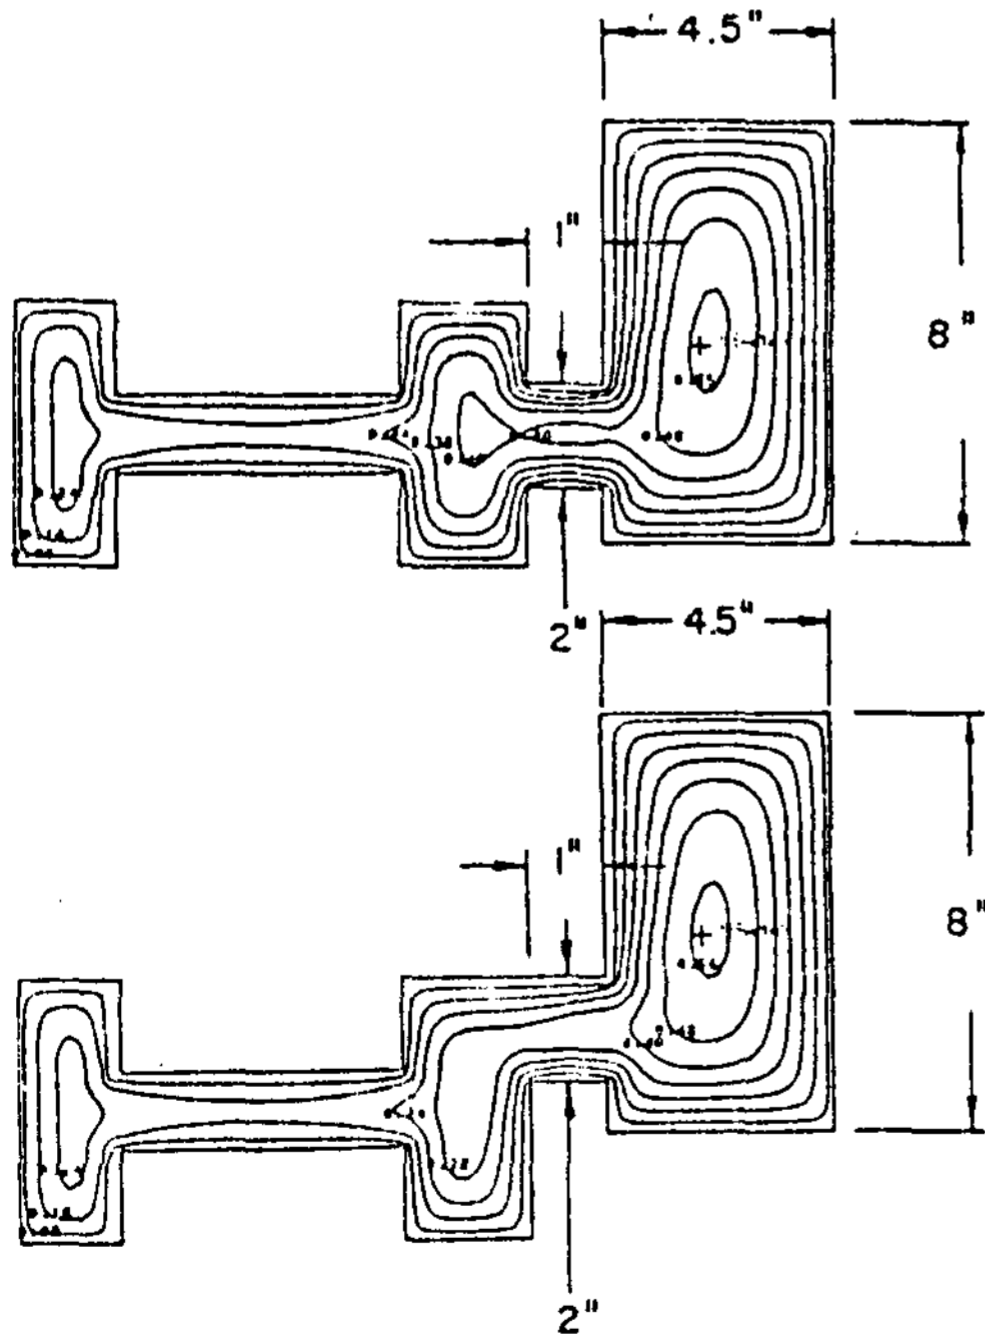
그림 12의 gear blank casting에서 riser contact 위치에 따르는 응고곡선의 변화.
